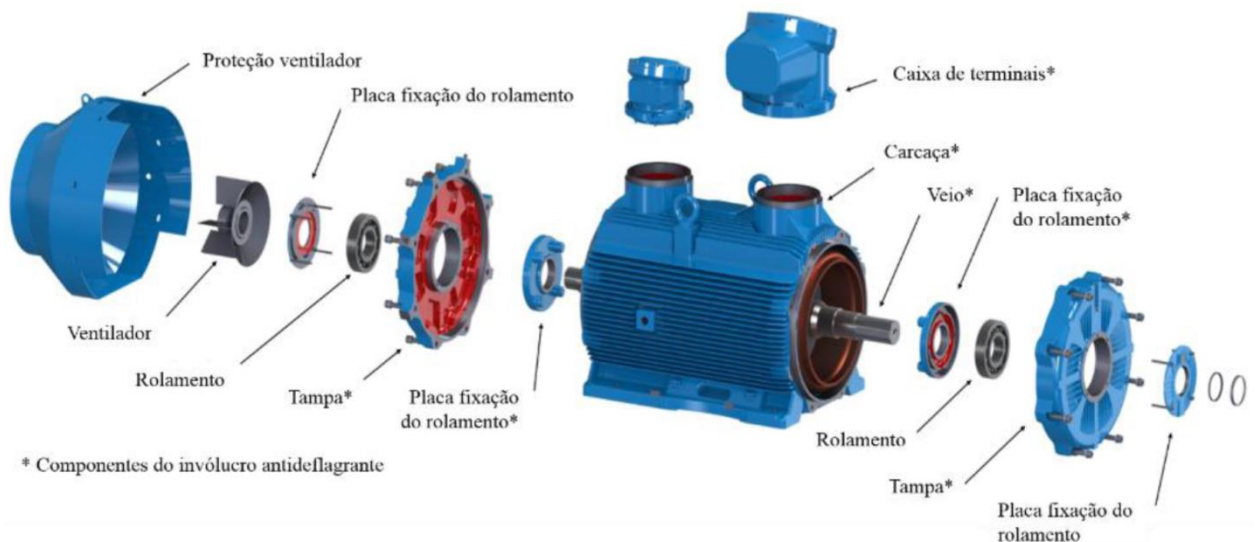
Vista explodida de um motor de indução trifásico antideflagrante
